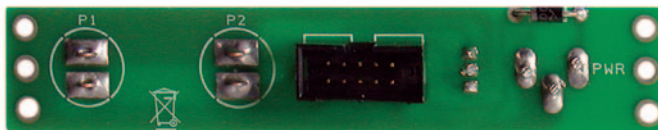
Photo d'un des prototypes de la platine de la section Poussoirs du commutateur vidéo.
